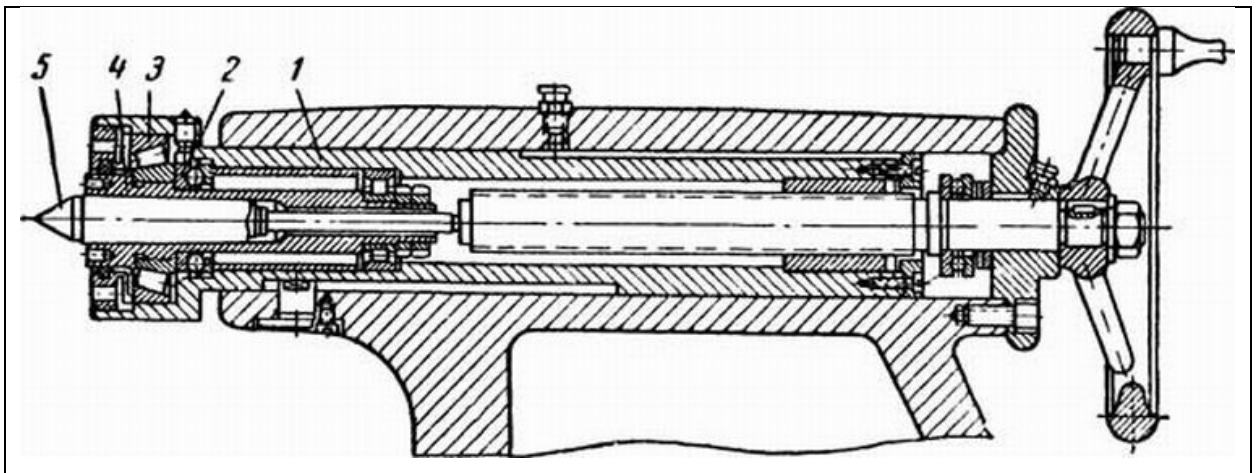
Установка оборотового заднього центру в пінолі задньої бабки
